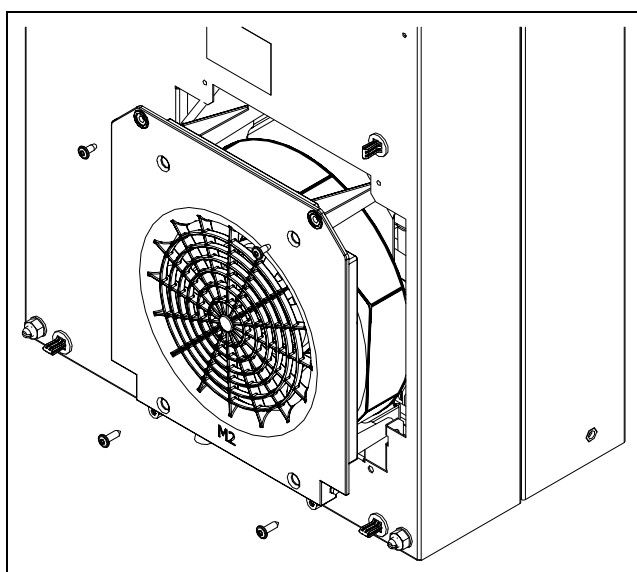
démonter le ventilateur du circuit externe (4 vis à dévisser)
